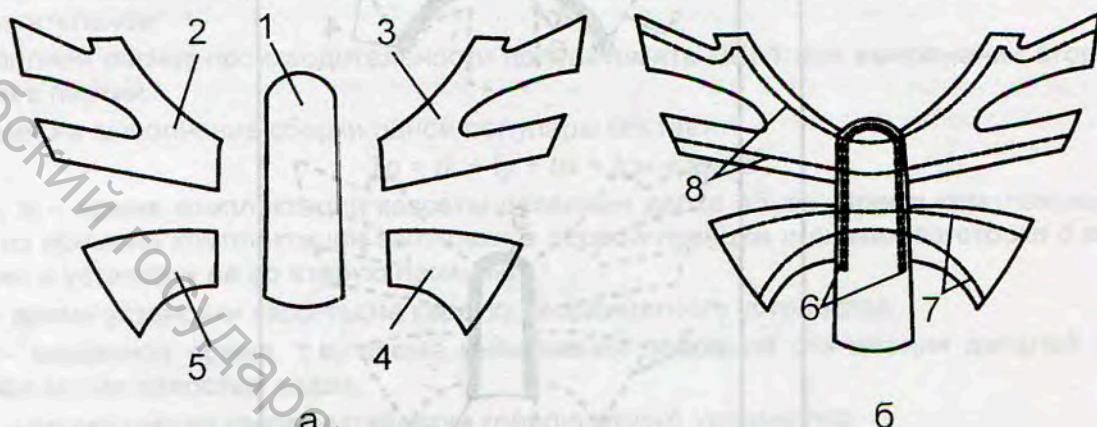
Конструкция заготовки верха сандаальной обуви
